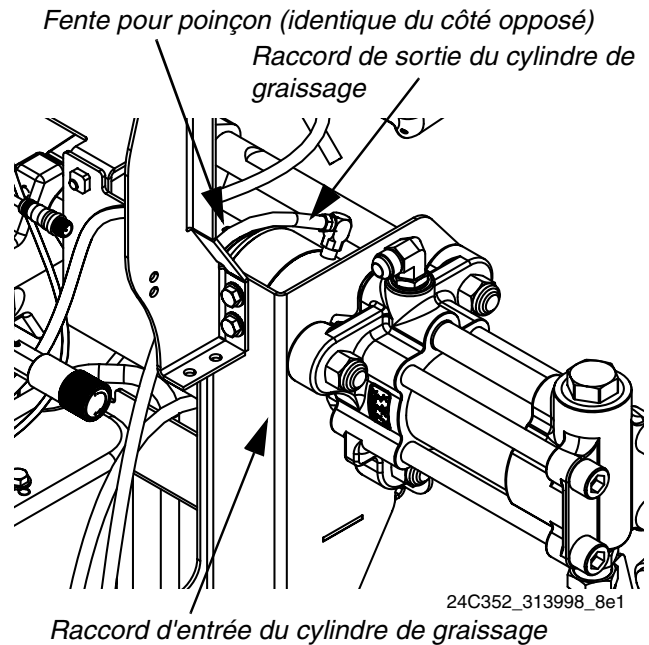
Cylindre de graissage, vu de l'arrière gauche de la machine
